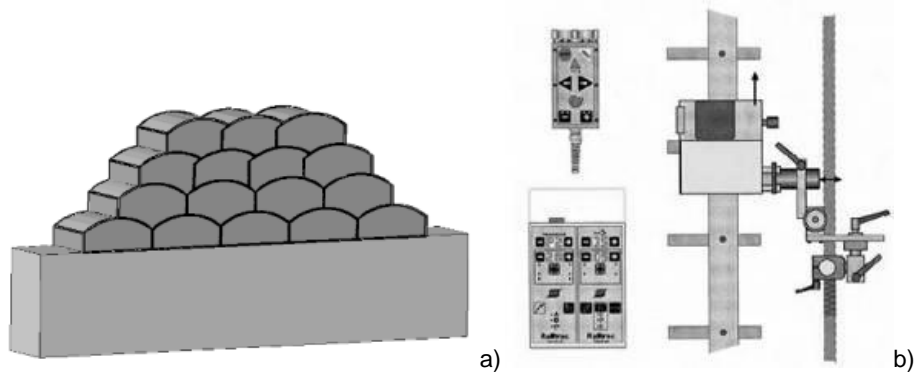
a) Secuencia de soldadura, b) Equipo Railtrac FW1000
